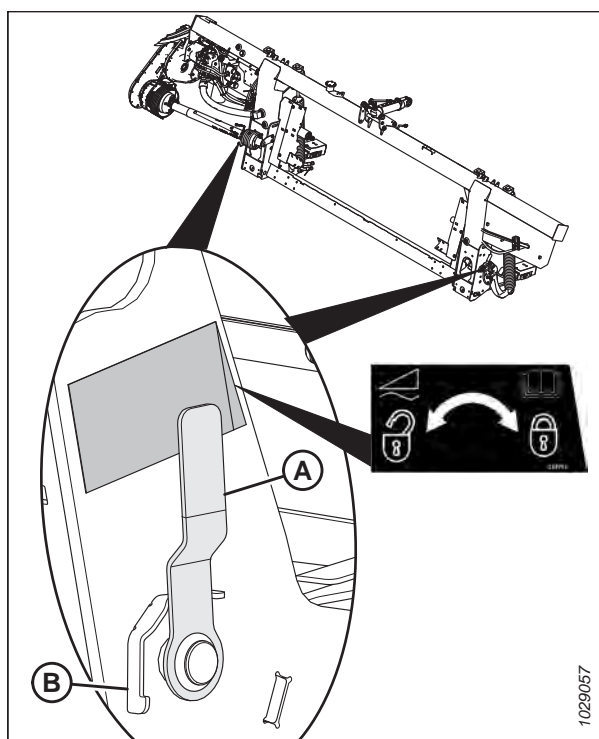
Dispositivo di bloccaggio flottazione della testata in posizione di blocco
